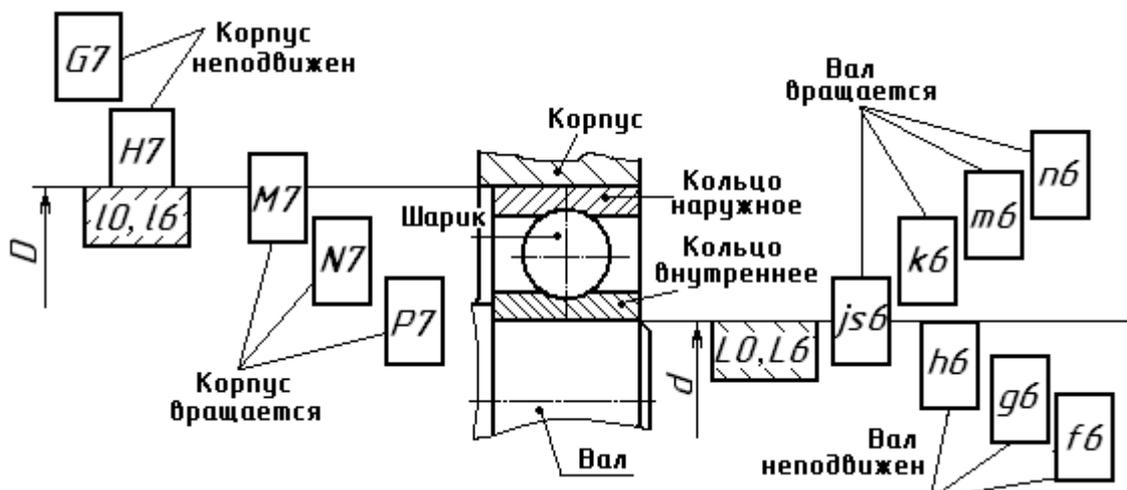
Посадки подшипников качения классов точности 0 и 6
